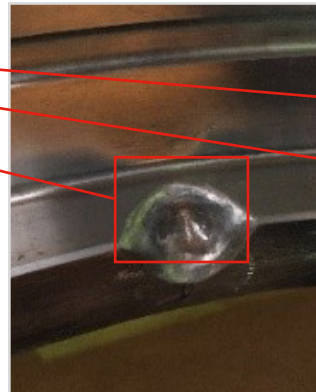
Beseitigung des Fehlers und Schweißen
